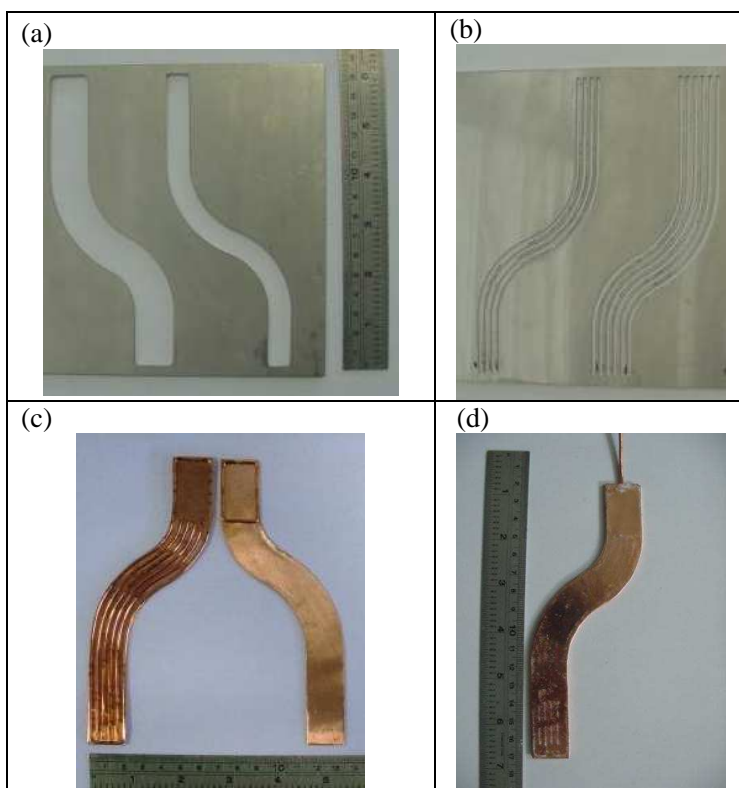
(a) Molde para a conformação da borda, (b) Molde para a conformação dos fios, (c) Etapa pré-soldagem a ponto, (d) Minitubo de calor após o processo de soldagem por difusão.
